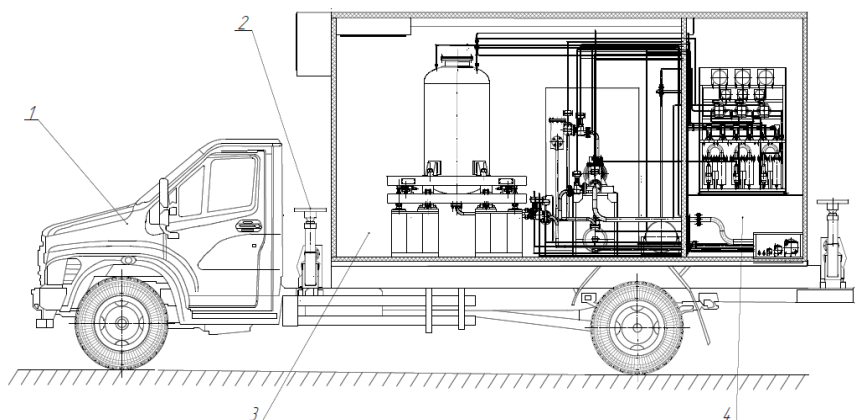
Подвижный агрегат контроля стационарных средств заправки и дозирования компонентами ракетного топлива:
